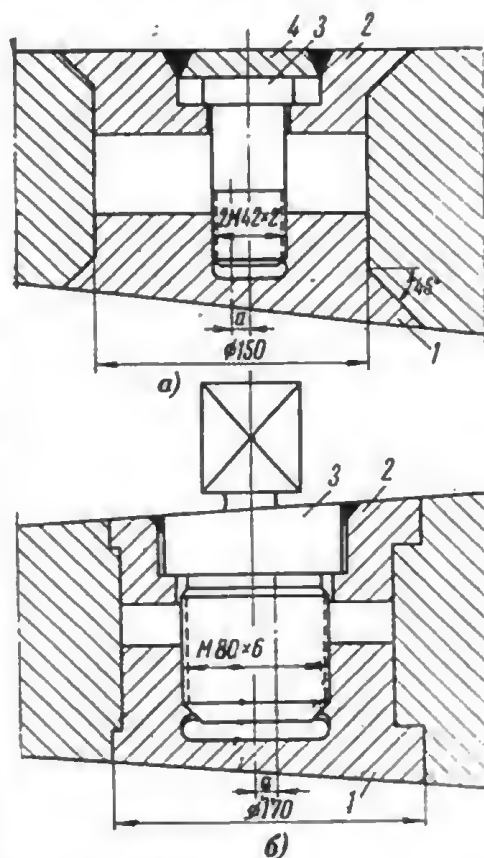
Заглушки монтажных отверстий лопастей рабочего колеса. а — старая конструкция заглушки; б — новая конструкция заглушки; 1, 2 — нижняя и верхняя заглушки; 3 — болт; 4 — крышка.
